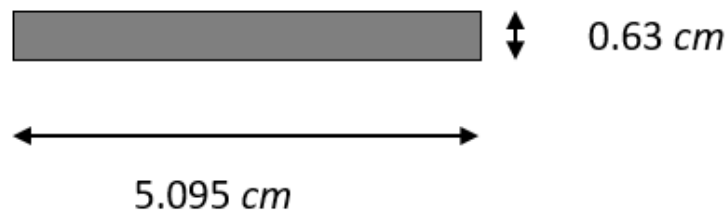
Sección transversal de la barra metálica Tipo 02
